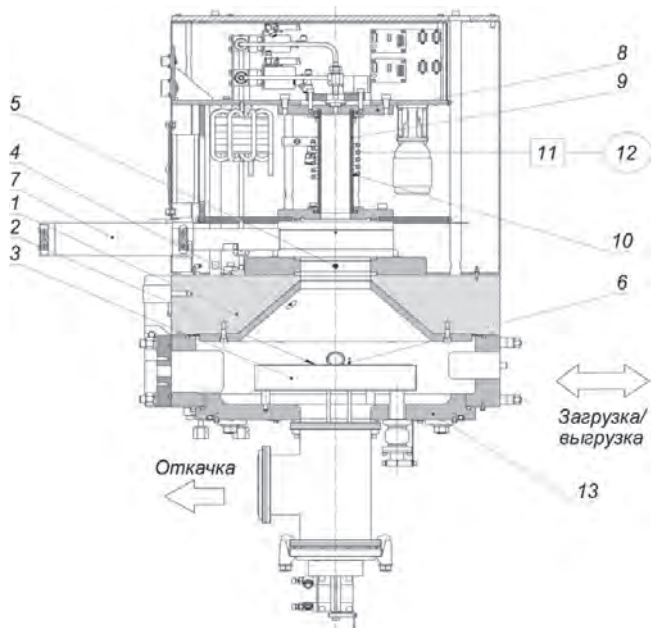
Конструкция реактора установки АСО (1 — верхняя камера; 2 — кремниевая пластина диаметром 200 мм; 3 — подложкодержатель; 4 — отверстие для подачи прекурсоров; 5 — отверстие для подачи продувочного газа; 6 — механизм вертикального перемещения; 7 — вакуумный клапан; 8 — источник плазмы; 9 — керамическая колба; 10 — индуктор; 11 — согласующее устройство; 12 — ВЧ-генератор; 13 — соединительный фланец подложкодержателя)
